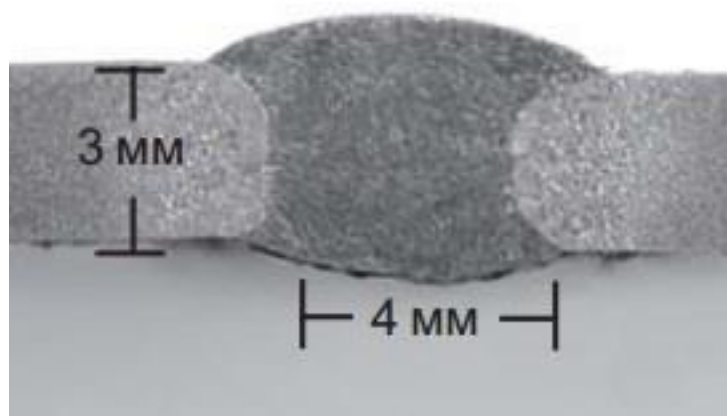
SpeedRoot: Микрошлиф сварного соединения
